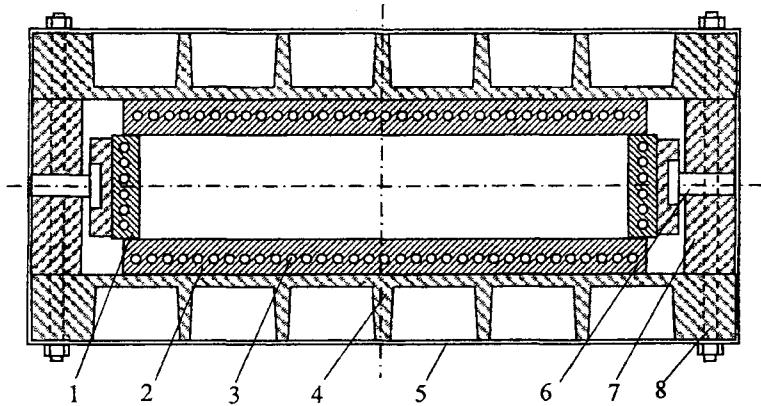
Схема сборного слябового кристаллизатора (в поперечном разрезе) с толстыми медными стенками:
